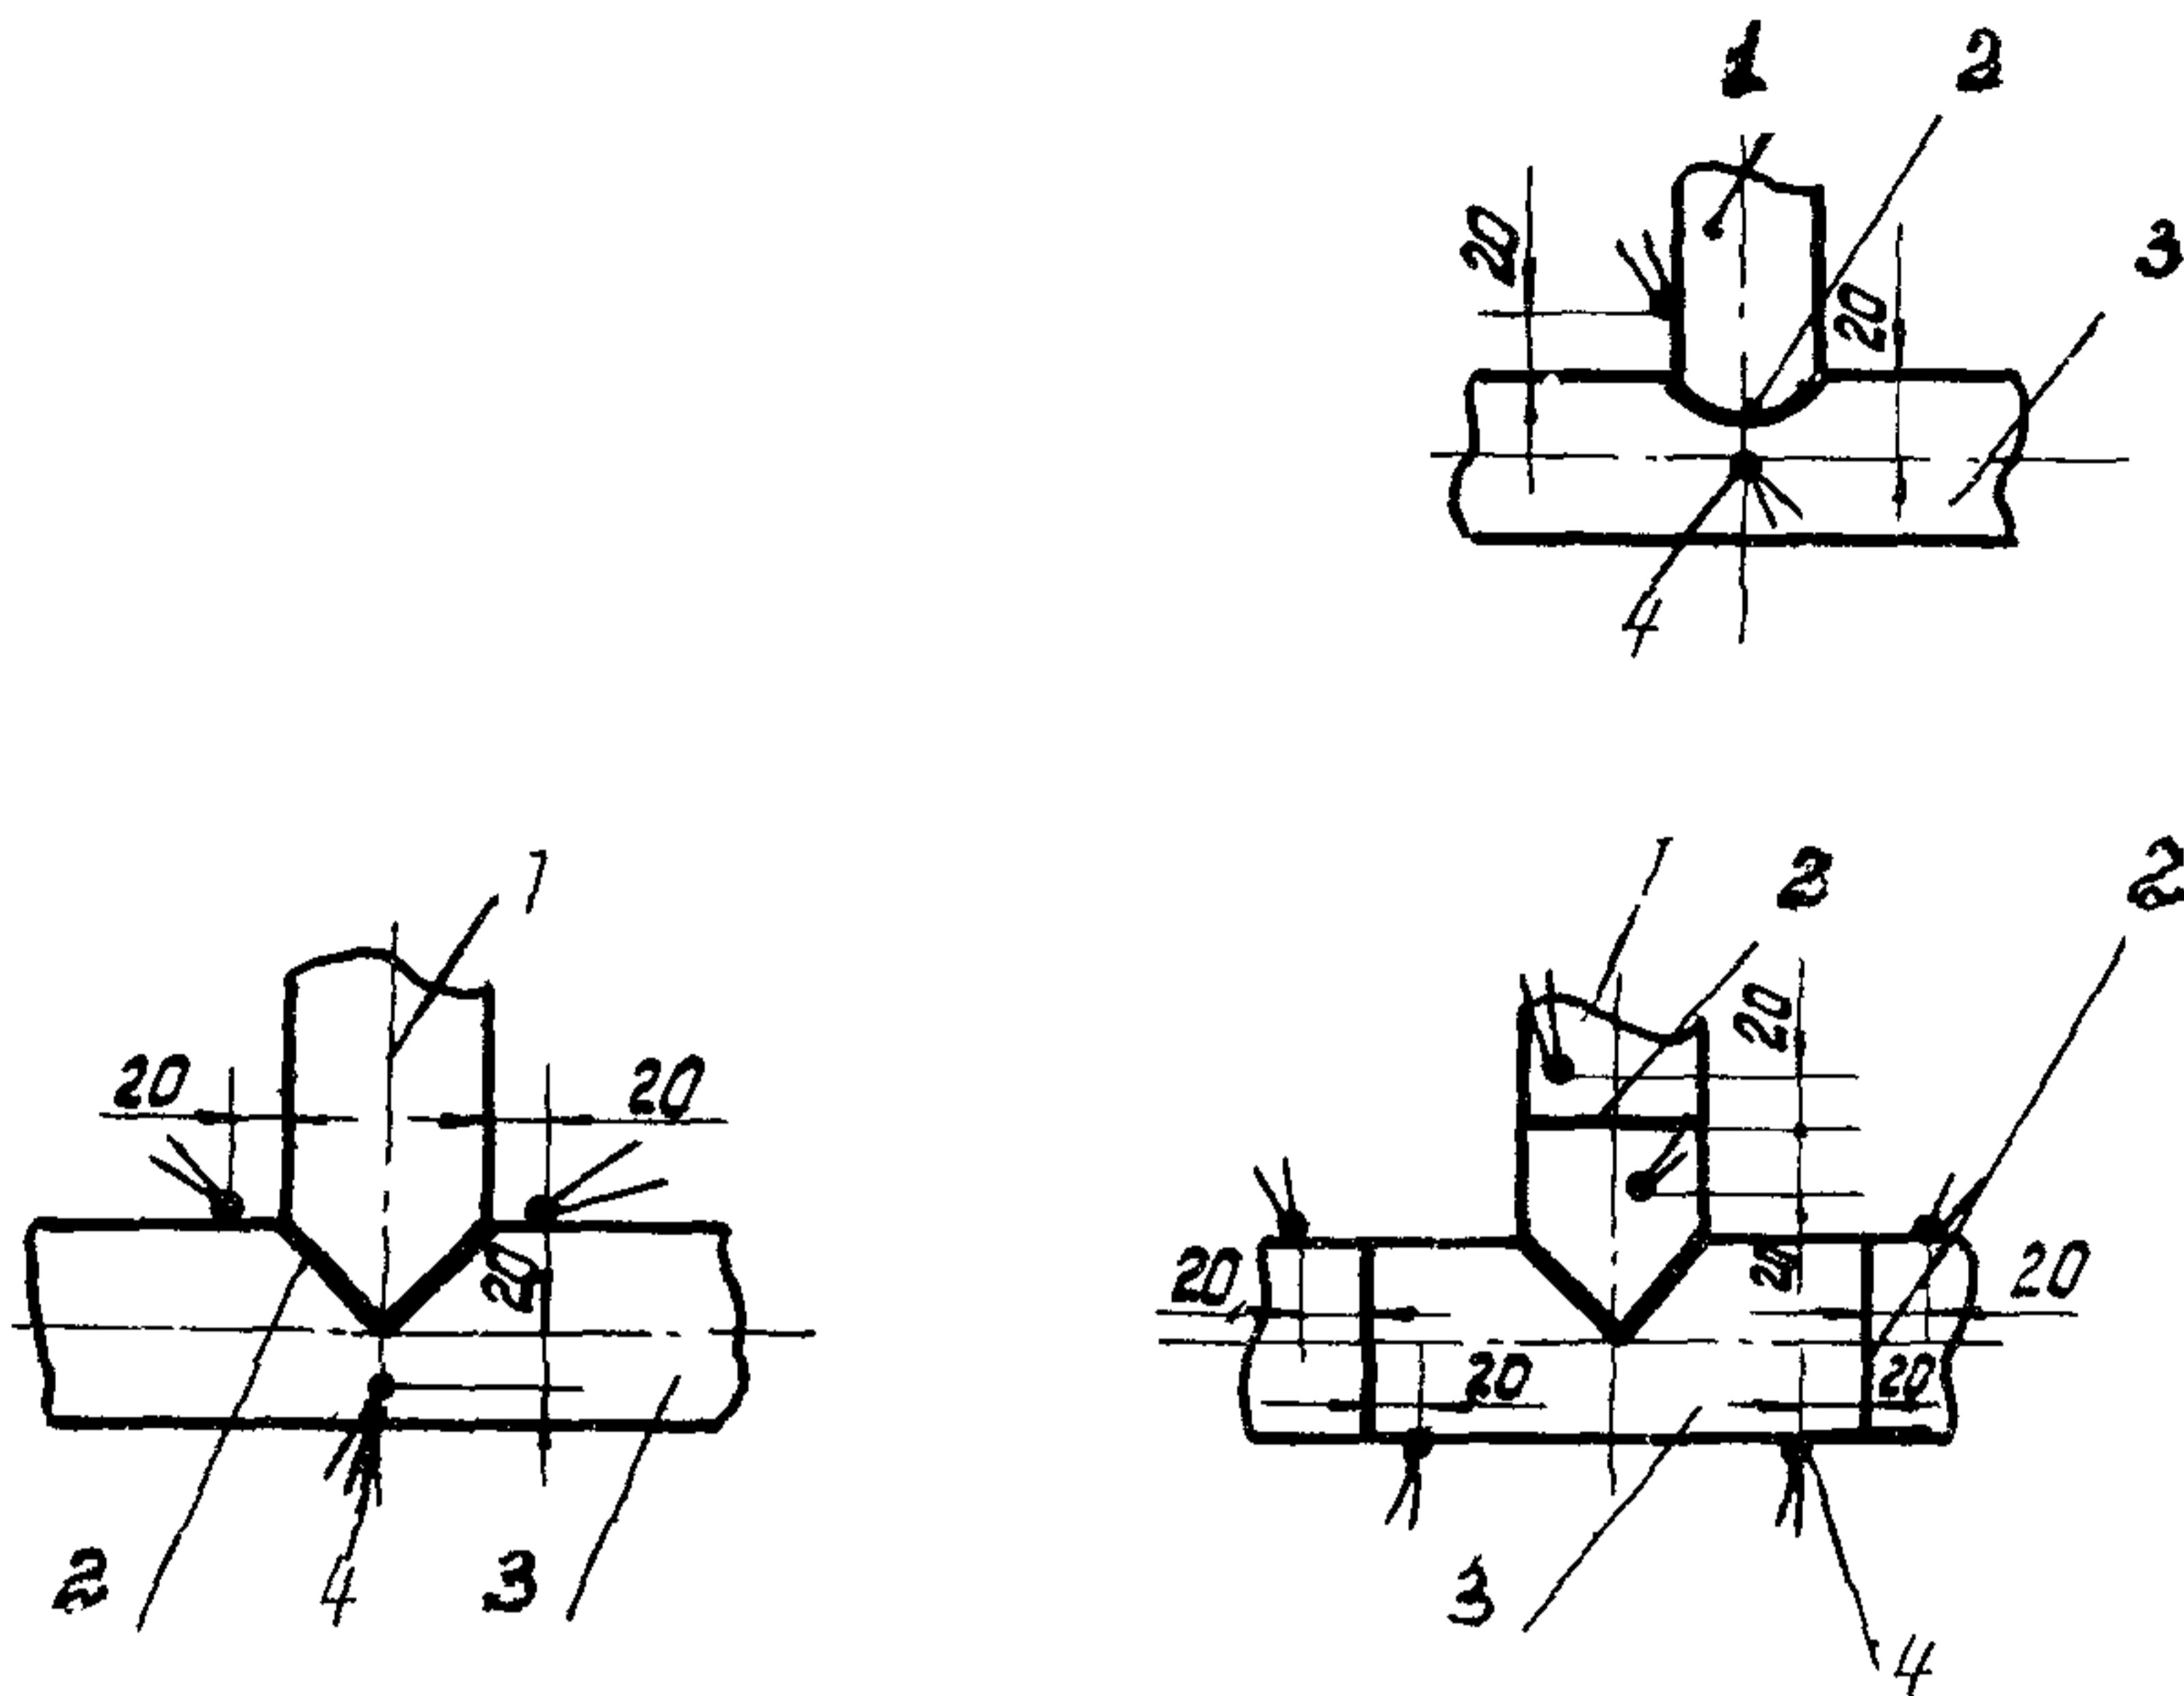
Рис. II. Количество термометров, необходимых для контроля температуры и схемы их установки на сварных соединениях тройников и тройниковых соединений различной конструкции:
